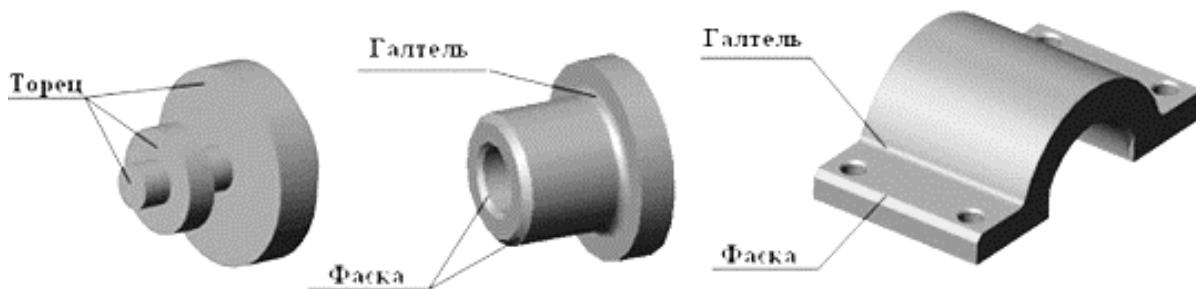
Образец выполнения конструктивных элементов деталей.
